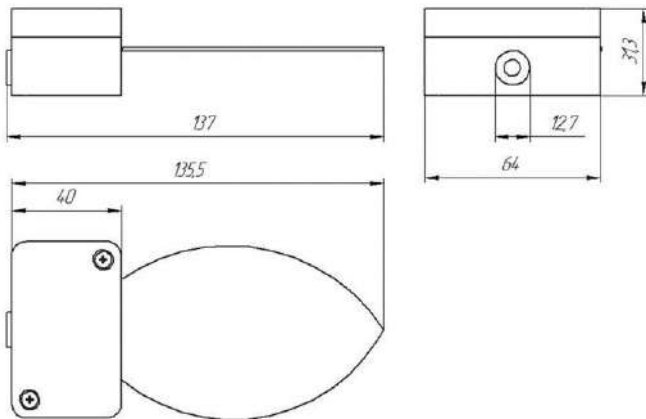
Габаритные размеры изделия «СОКОЛ-ДВЛ».
